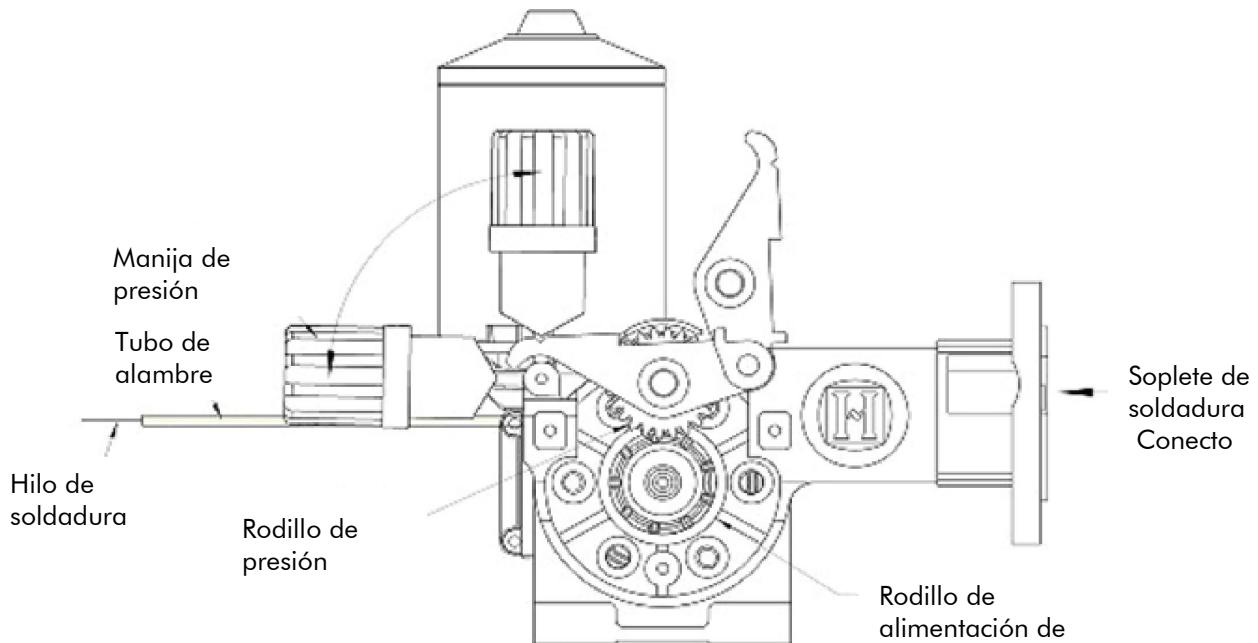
Diagrama de instalación del alambre de soldadura
